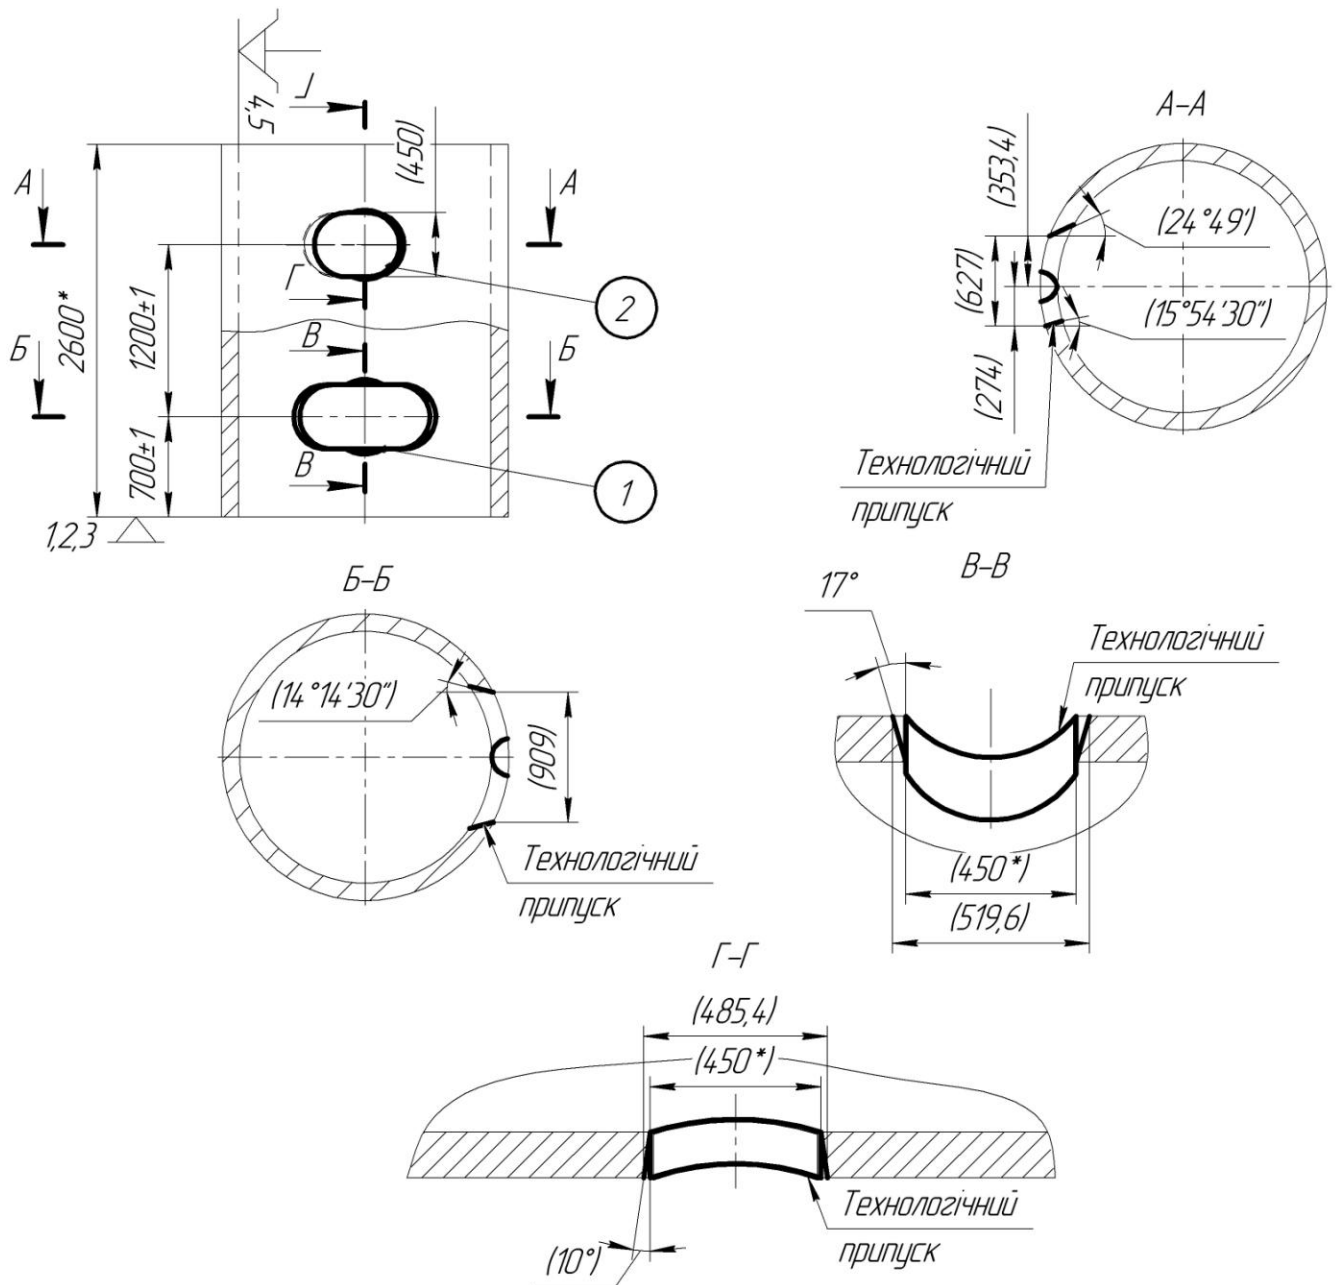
Схема базування заготовки на вертикально-фрезерній з ЧПК операції (другий варіант)
